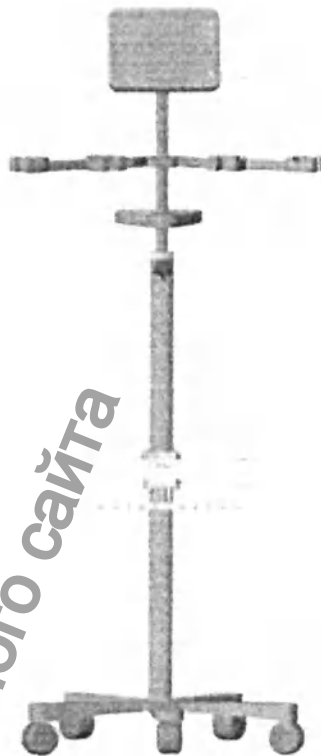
Вид медицинской стойки Endostand в сборе
